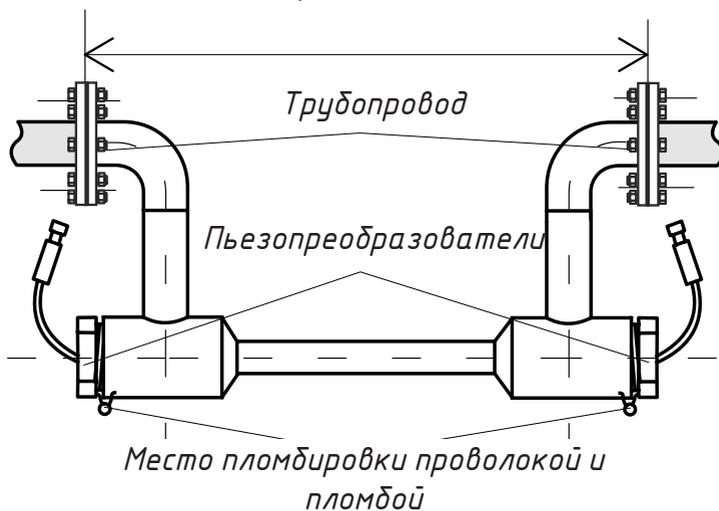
в - УПР изготовленные из нержавеющей стали, резьбовые, литые.
